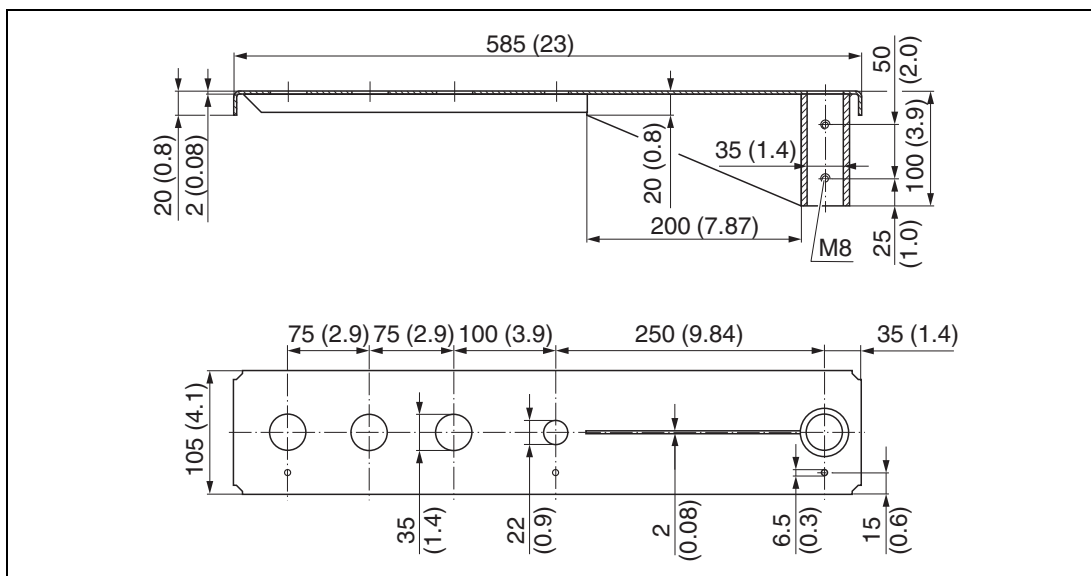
Abmessungen Ausleger (kurz) schwenkbar für Sensor Prozessanschluss Rückseite, Maßeinheit: mm (Zoll)
